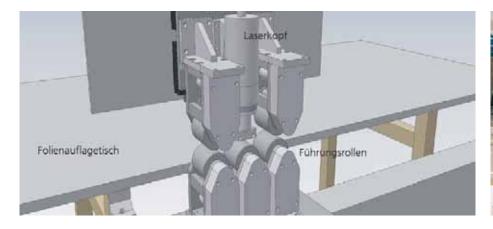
CAD-Modell des Schweißsystems (Prototyp).
